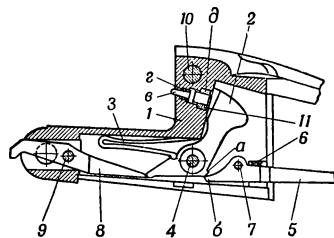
Коленчатая колодка дробового двуствольного ружья. Модель ИЖ-49, с ударными механизмами, расположенными внутри корпуса коробки после модернизации:
